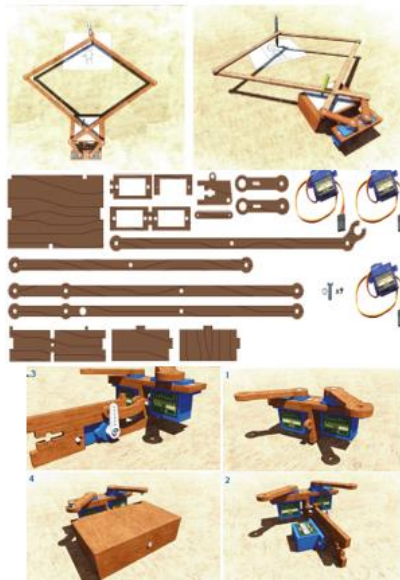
Diseño 3D, piezas y armado en SketchUp
